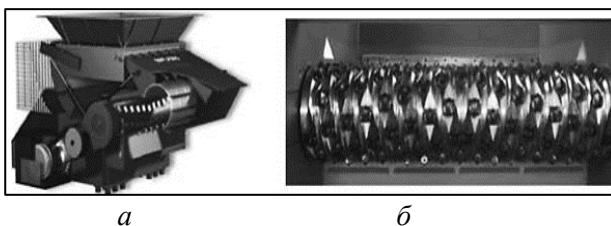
, а – общий вид однороторного шредера; б – рабочий орган одноножевого ротора
